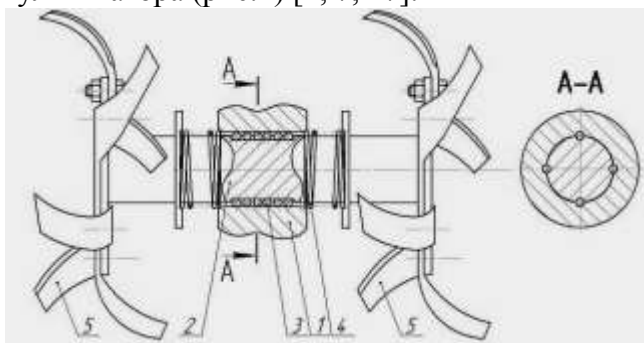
Принципиальная схема секции фрезерного культиватора для междурядного возделывания почвы : 1 – опора, 2 – вал, 3 – шарики, 4 – пружина, 5 – фреза
